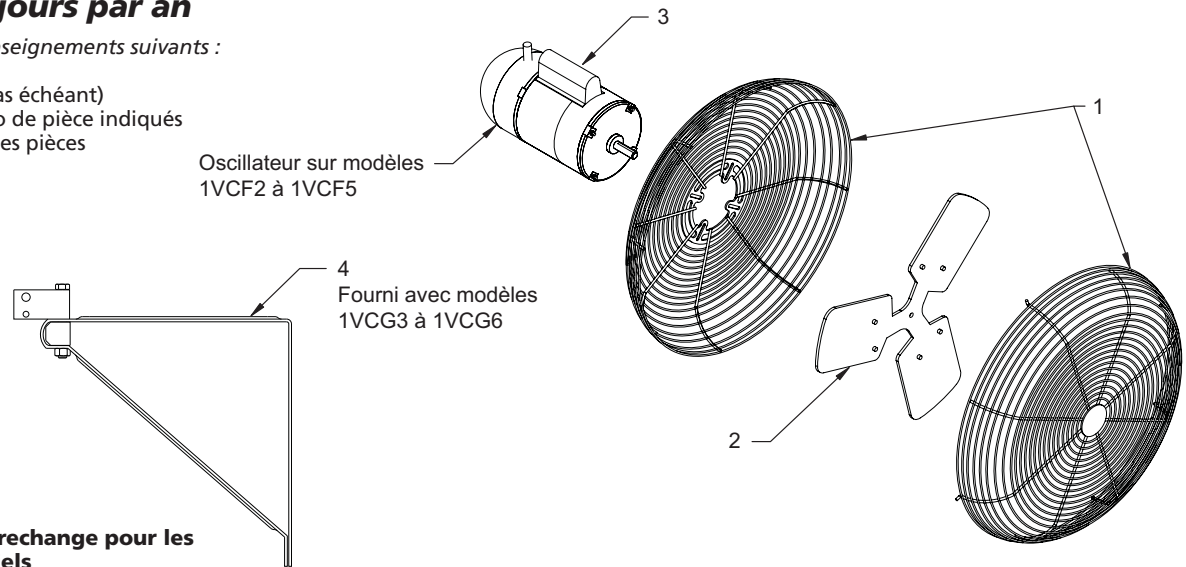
Pièces de rechange pour les ventilateurs industriels
